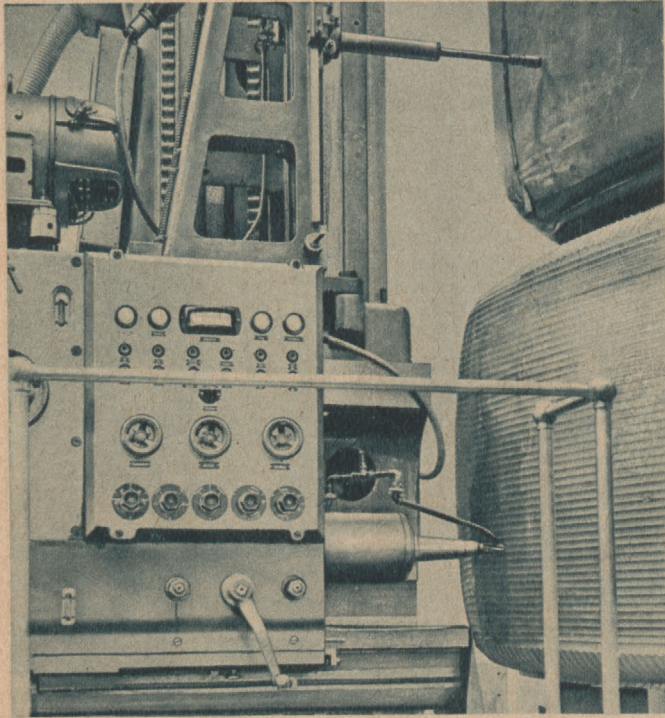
Gesenkräsmaschine mit elektrischer Fühlersteuerung (Siemens)
